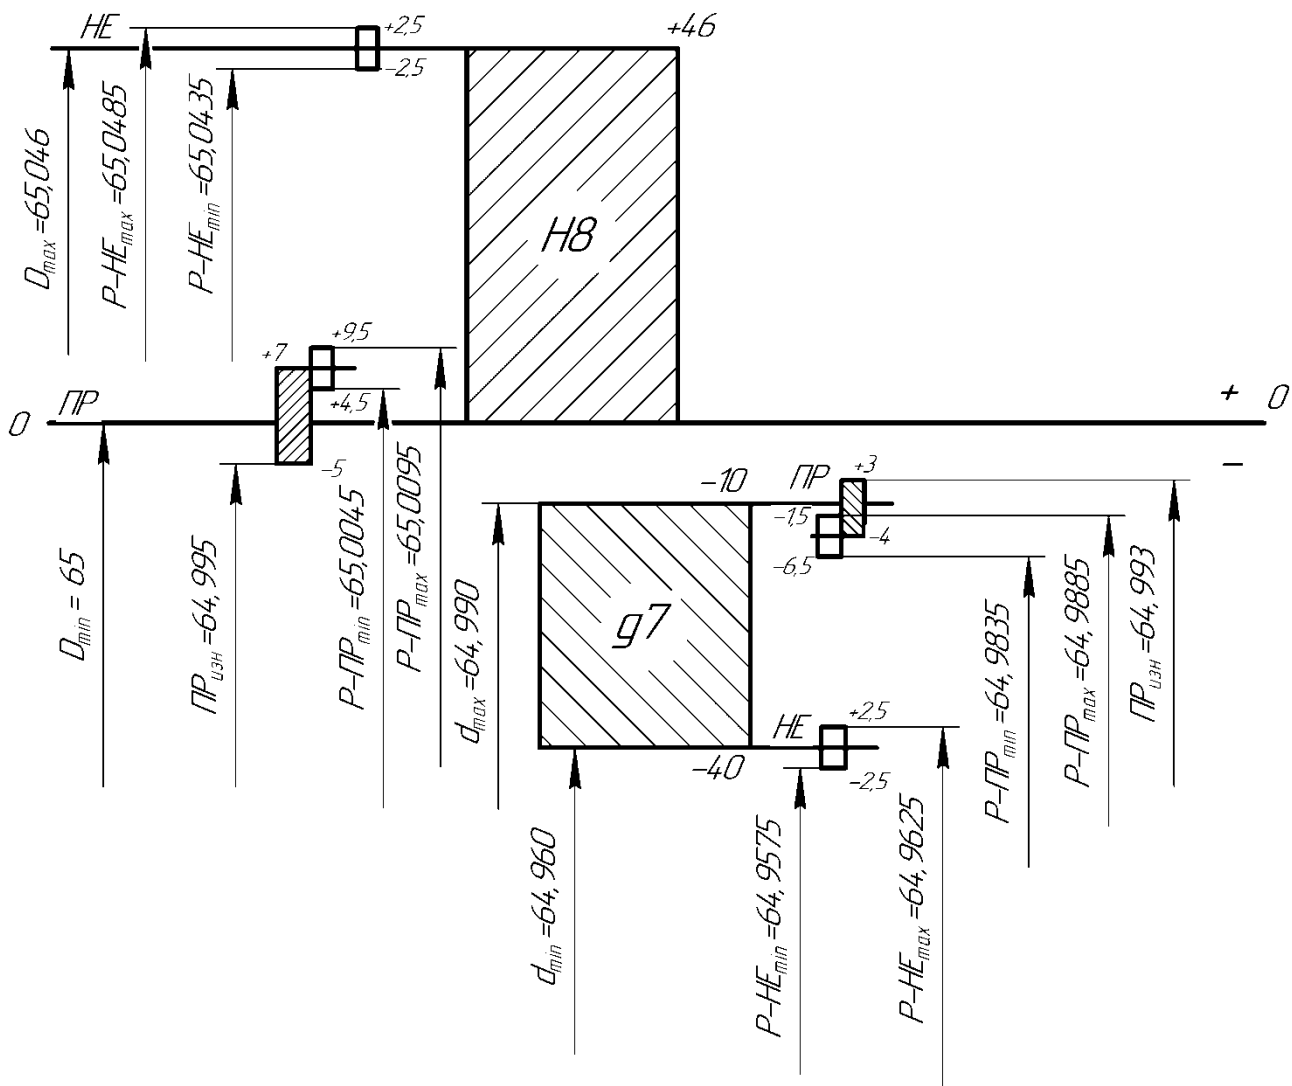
Схема расположения полей допусков рабочих калибров для сопряжения $65 \frac{H8}{g7}$
